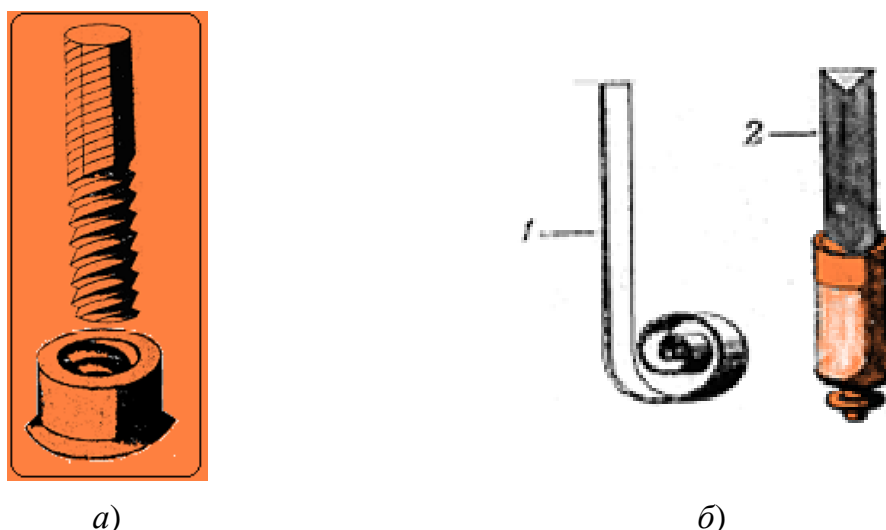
Эскиз винта с гайкой (а) и инструментами для разметки и изготовления винта (б) (Жак Бессон, 1569 г.):
